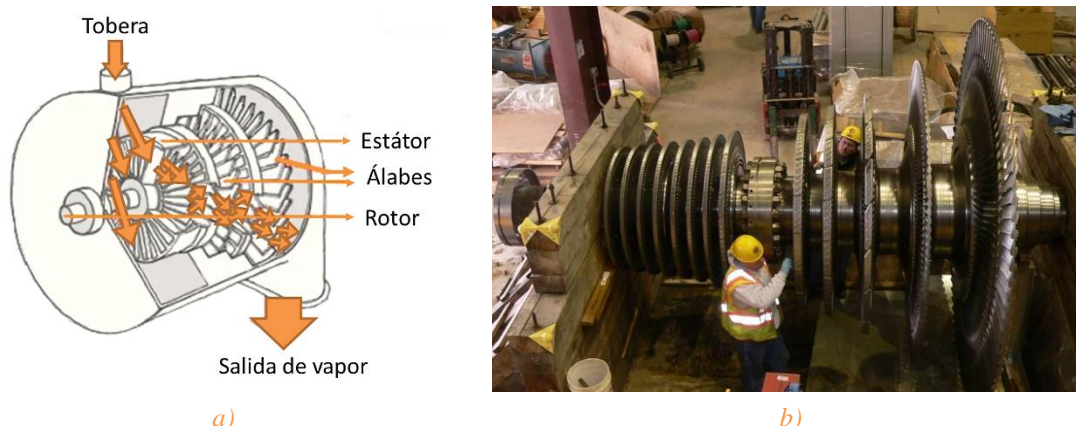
a) Esquema de las partes de una turbina de vapor [20] e b) imagen de una turbina de vapor real [21].
